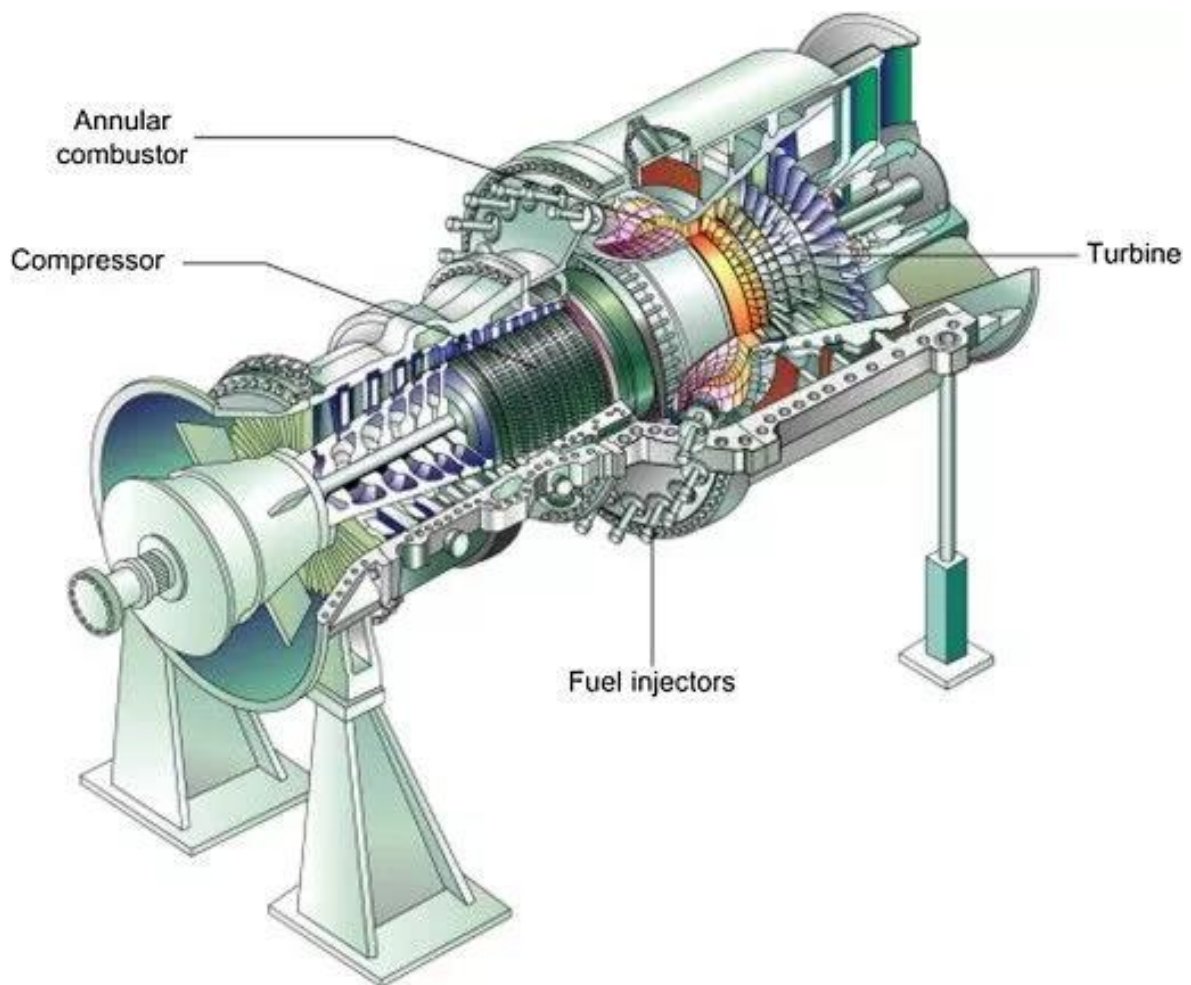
Componentes turbina de gas (fuente: [3])
